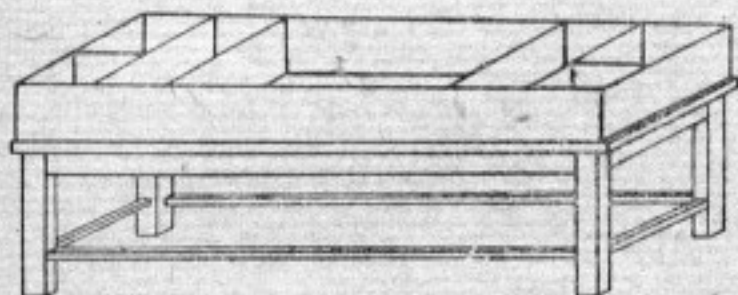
Стеллаж — ящик для мелких и крупных деталей
